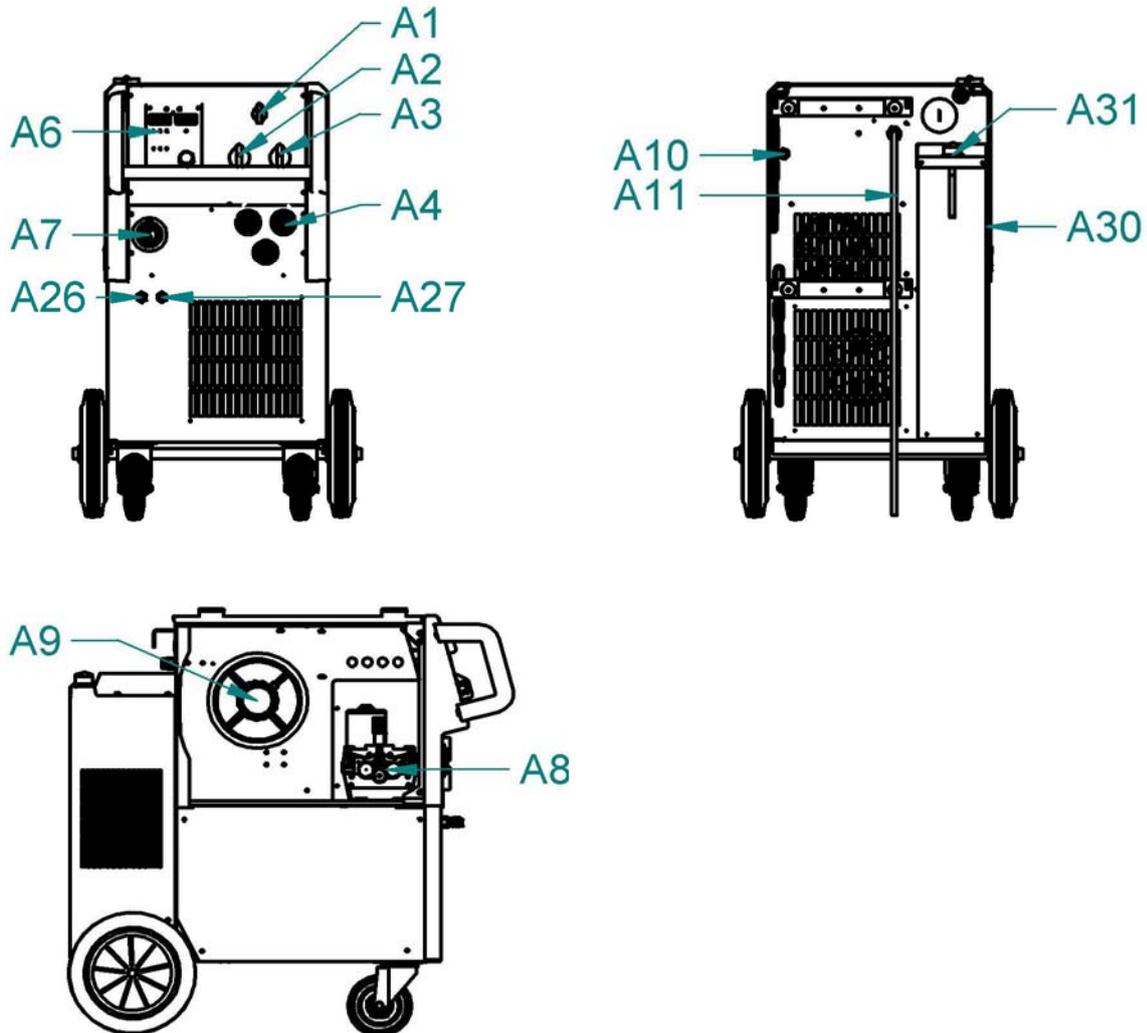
Hauptteile der Maschine Ryval 400-500 aXe Compact
